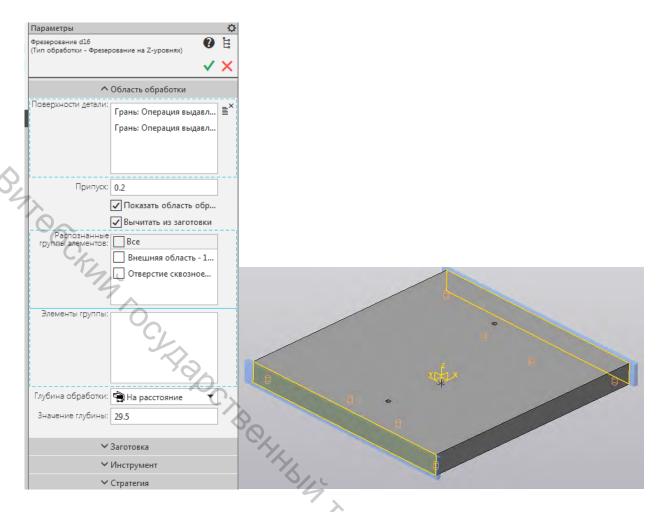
Создание операции фрезерования торцов заготовки
